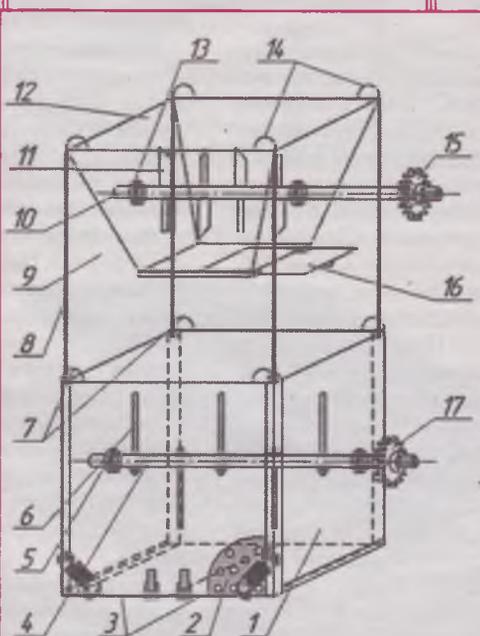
Установка для компостирования растительных материалов: 1 – контейнер; 2 – перфорированные листы; 3 – днище; 4, 10 – горизонтальные валы; 5 – подшипник; 6 – пальцы; 7 и 14 – проушины; 8 – стойки; 9, 12 – бункеры; 11 – ножи; 13 – подшипники; 15 и 17 – звездочки; 16 – заслонка
